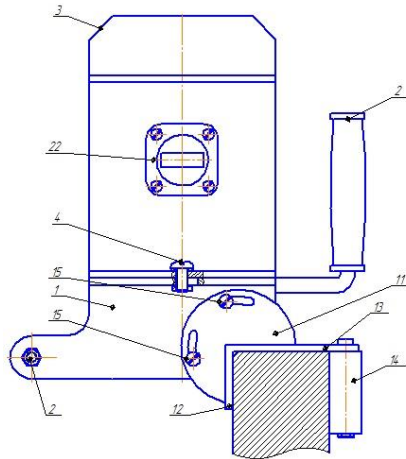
Конструкция модернизированного кромкофрезера (общий вид)
